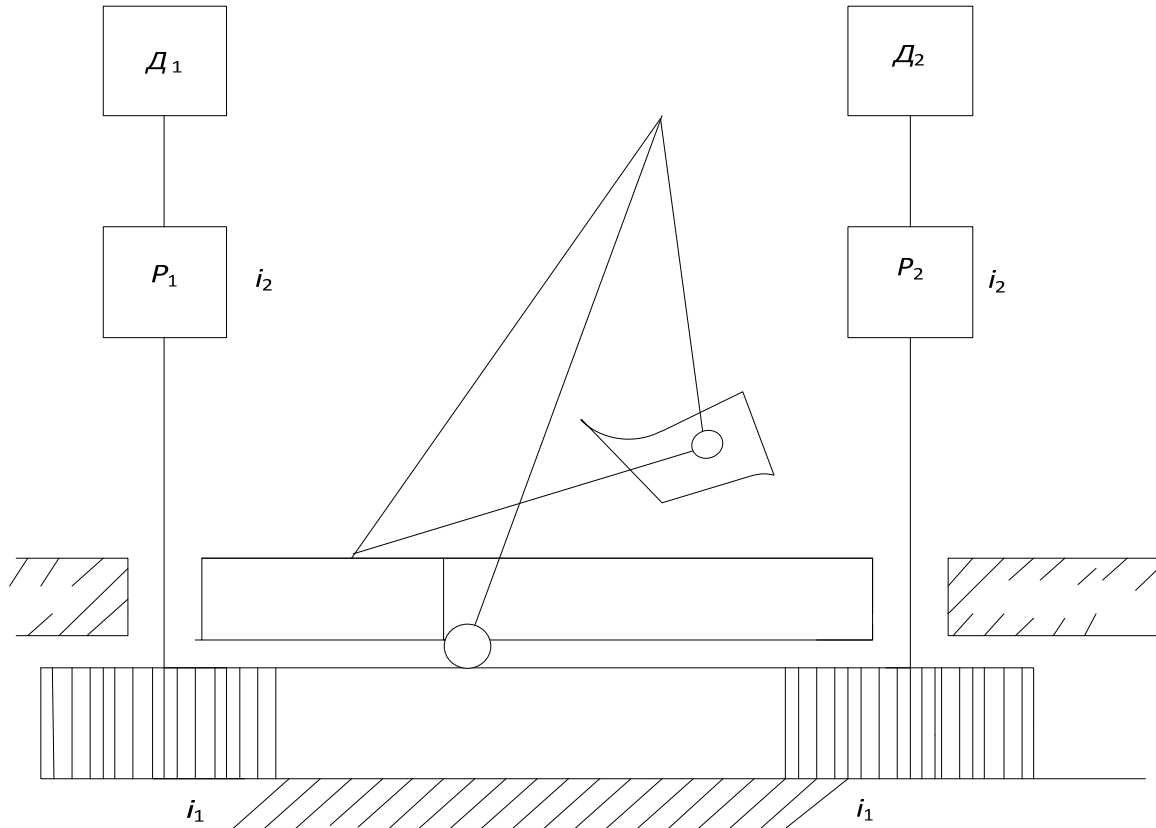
Конструкція механізму поворотної платформи екскаватора
